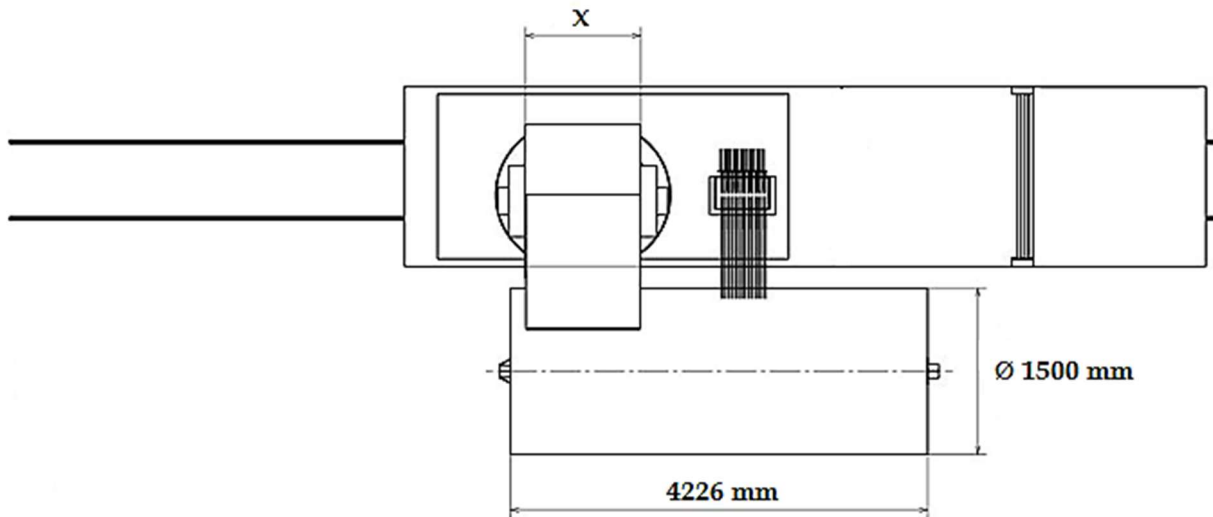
Vue de dessus de la solution d'enroulement des bobines d'âme.
